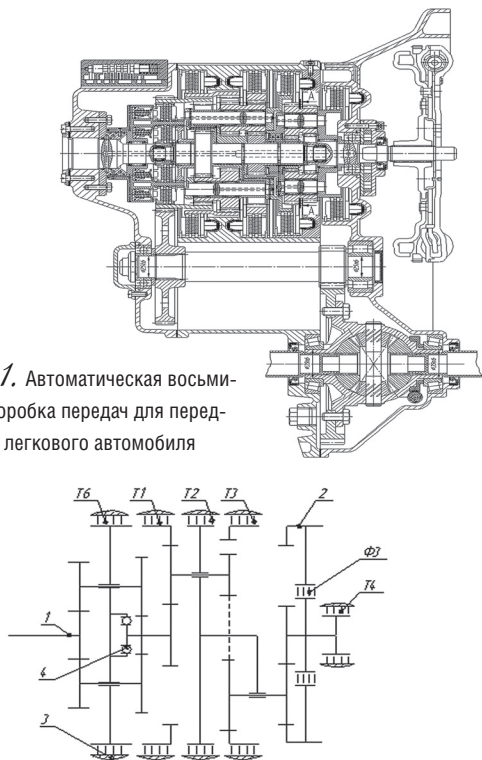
Кинематическая схема автоматической восьмиступенчатой планетарной коробки передач с двумя передачами заднего хода: 1 — входное звено; 2 — выходное звено; 3 — корпус коробки передач; 4 — муфта свободного хода; Ф3 — фрикционная блокирующая муфта; Т1, Т2, Т3, Т4, Т6 — фрикционные тормоза
